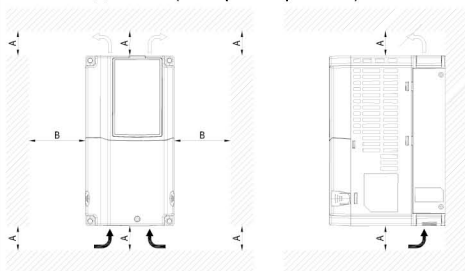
Несколько ПЧ: Установка без взаимовлияния (типоразмеры G, H)
